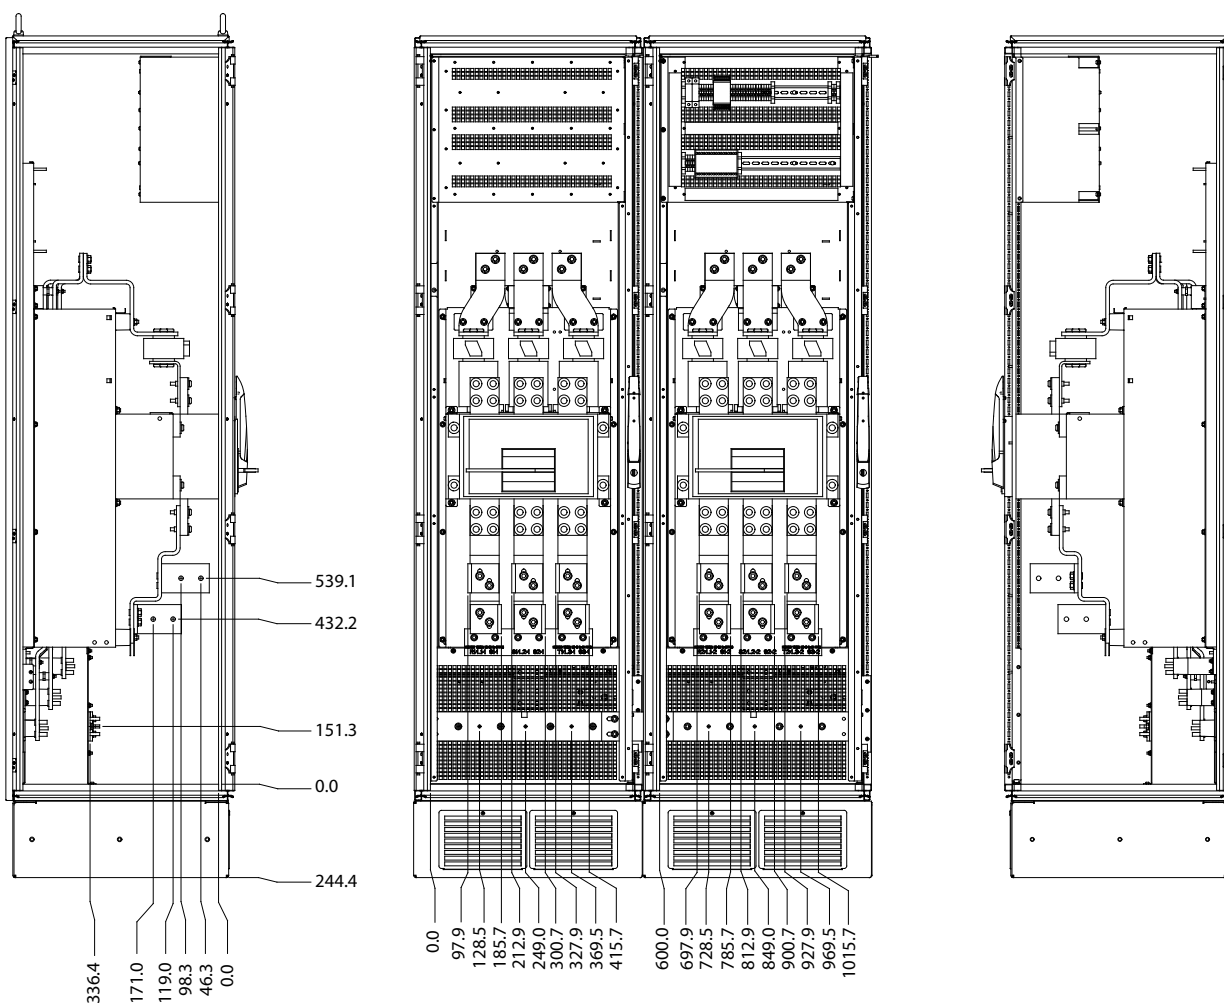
端子位置 — 左侧视图、正视图和右侧视图
